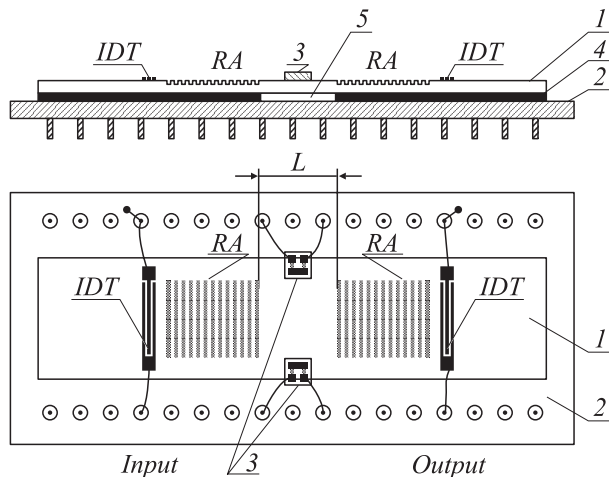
ПАВ-резонатор (1) с нагревателями на основании корпуса: 2 — основание корпуса; 3 — нагреватели; 4 — пластичная металлическая прокладка (индий); 5 — воздушный зазор.
